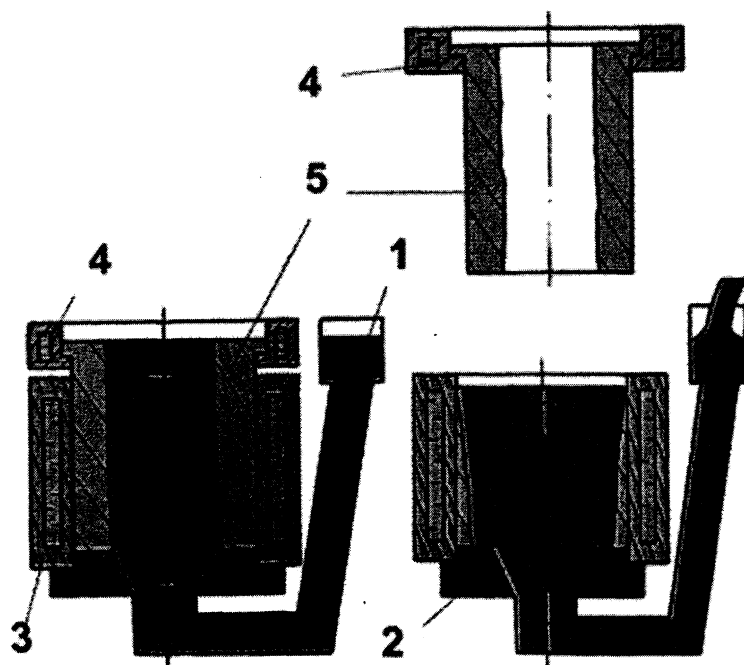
Принципиальная схема непрерывно-циклического литья полых заготовок без стержня: 1 – металлопровод; 2 – соединительный стакан; 3 – стационарная часть кристаллизатора; 4 – подвижная часть кристаллизатора (захваты); 5 – отливка
